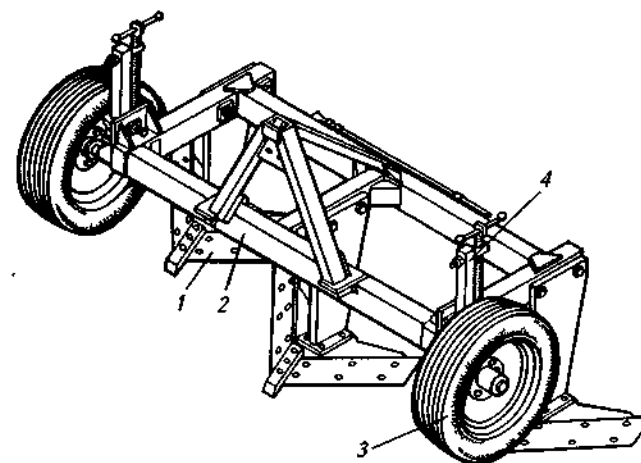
Плоскорез-глубокорыхлитель ПГ-3-100:
